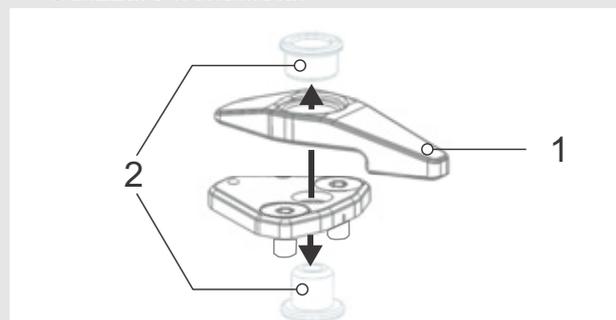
Collegamento della leva di sicurezza alla piastra di base
